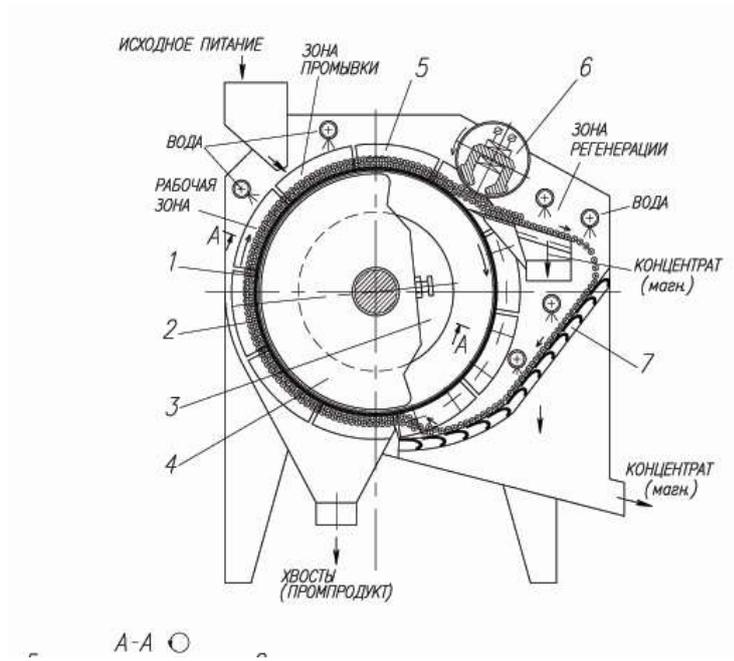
Барабанный сепаратор ВГСНПМП. 1- барабан сепаратора, 2 – слой шариков; 3- катушки возбуждения; 4 – магнитная система; 5 –реборды; 6- электромагнитный съёмник; 7 – шпальтовый грохот.
